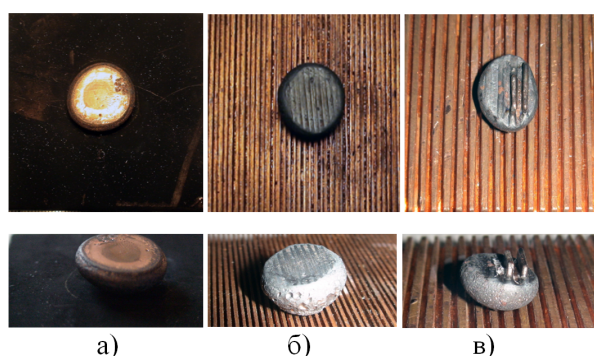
Состояние контактной поверхности капля меди, затвердевших на гладкой медной пластине (а), шероховатой с узкими (б) и широкими (в) пазами
